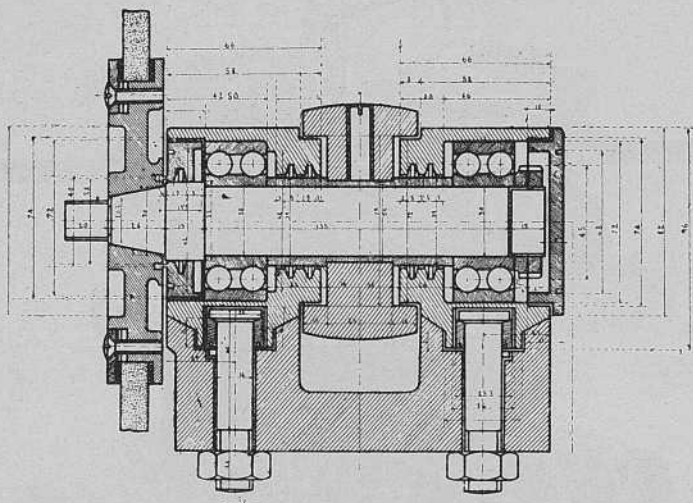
Eje portamuelas montado sobre cojinetes de bolas.
